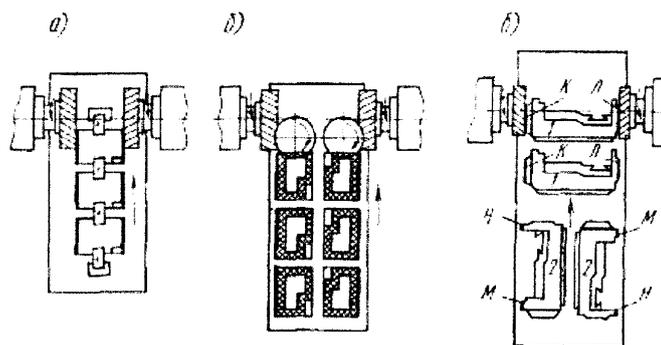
Групповая установка корпусных деталей на продольнофрезерном станке
